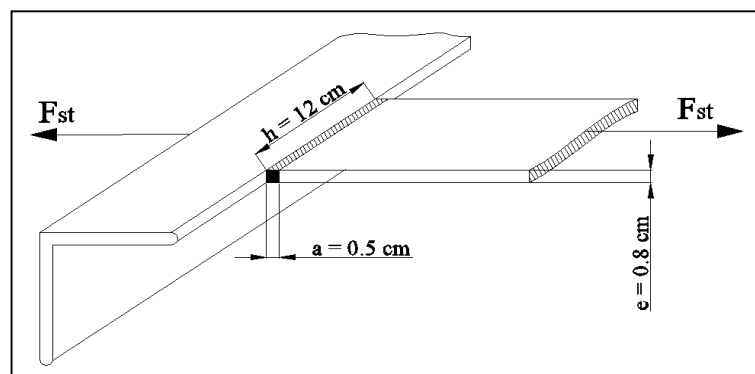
Fuerza de tracción en la soldadura
